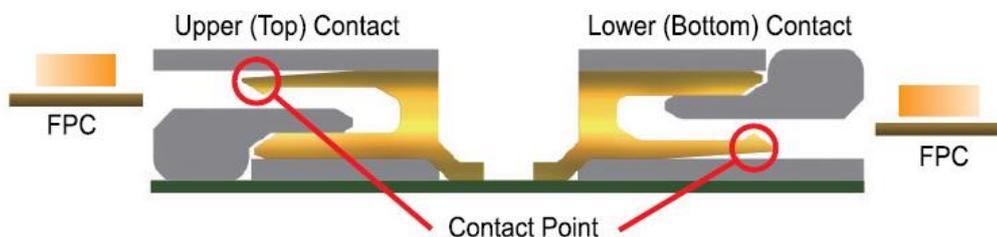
Соединители FPC с верхним и нижним расположением контактов
